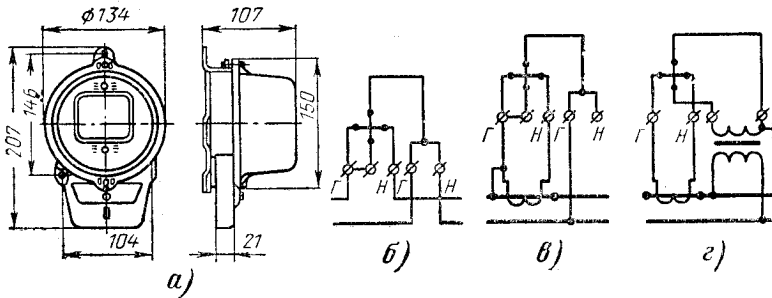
Габаритный чертеж и схема включения счетчика типа СО.
